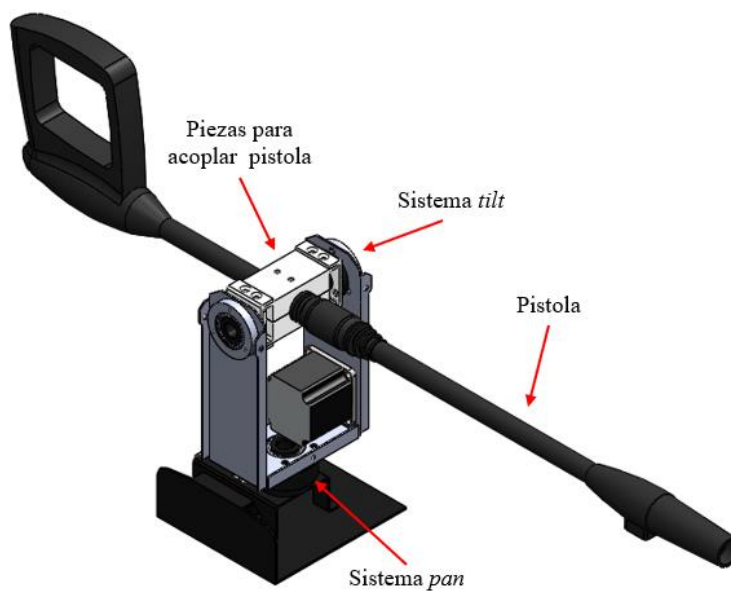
Vista isométrica del diseño CAD del sistema *pan-tilt* con la pistola de alta presión acoplada.
